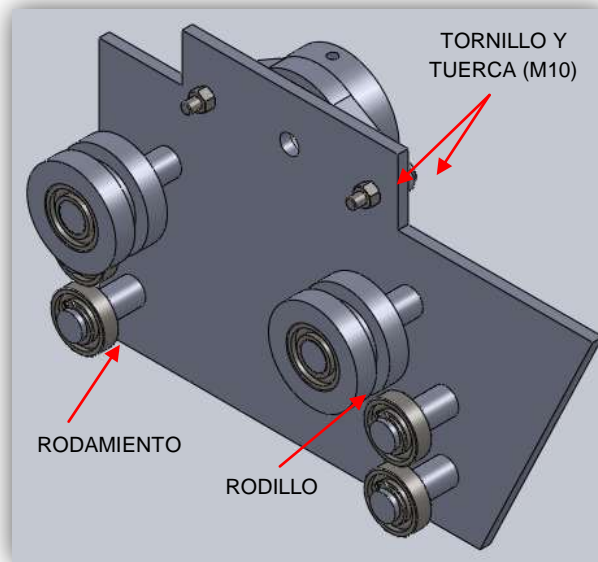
Ensamblaje estructura para desplazamiento en el eje “z”.
